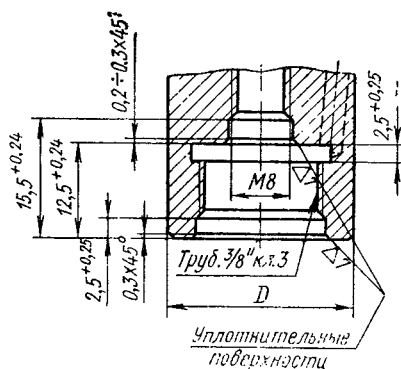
Присоединительные размеры головки резака под наружные и внутренние мундштуки
